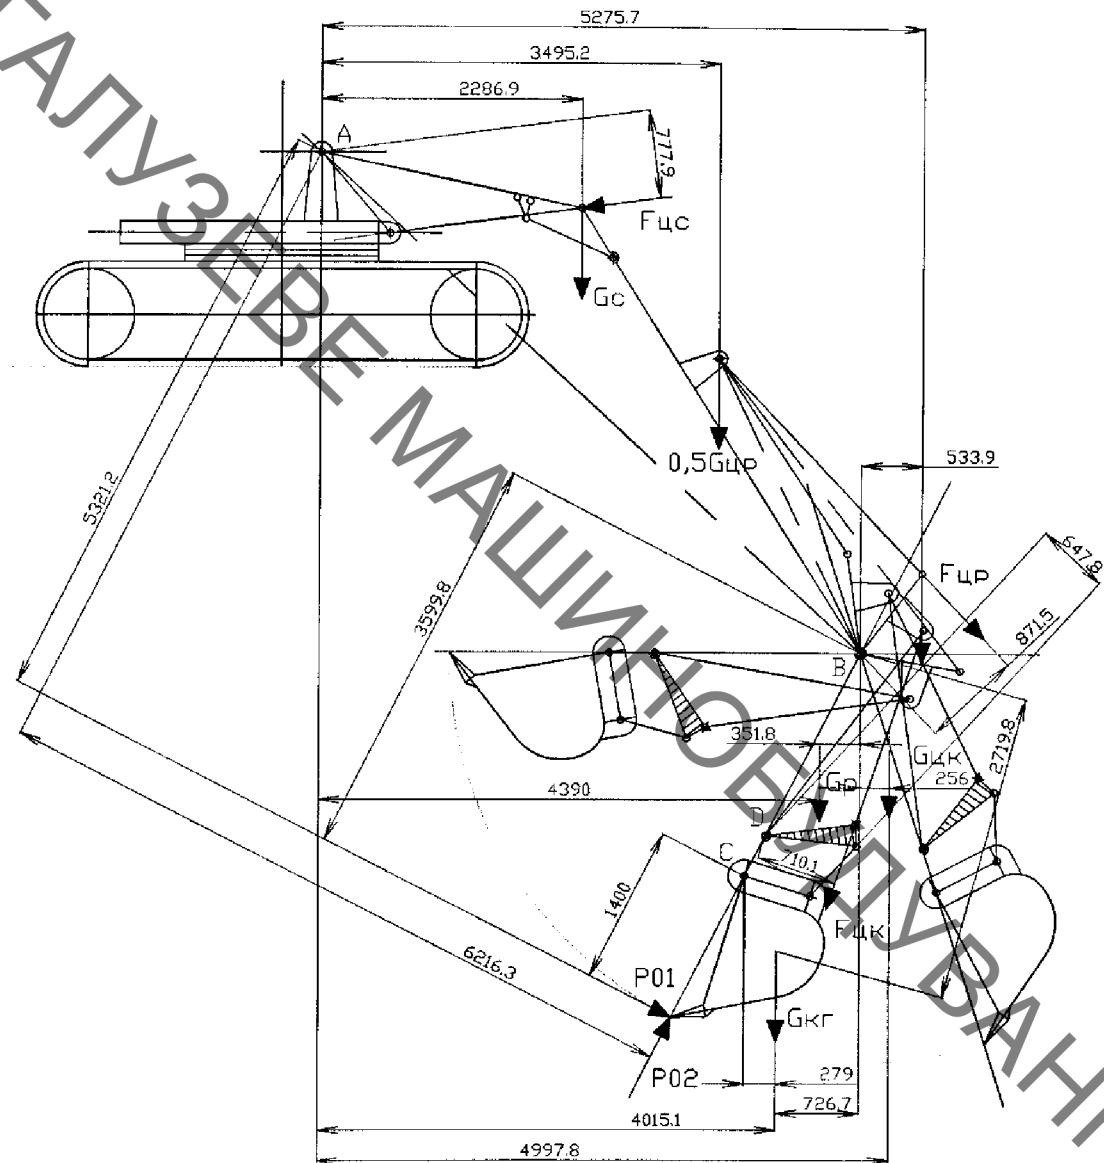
Розрахункова схема копання поворотом рукоятки
